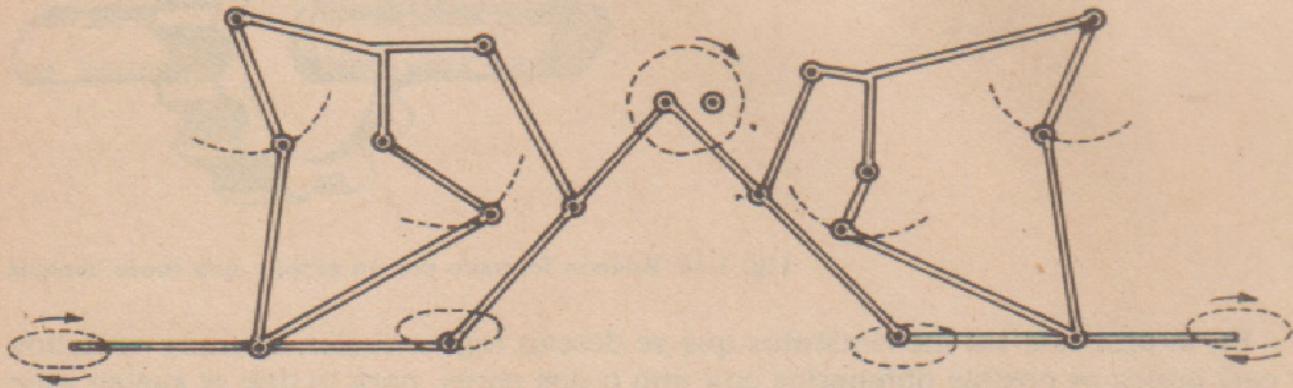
Mecanismo de Chevishev que reproduce el movimiento de las manos de un remero
